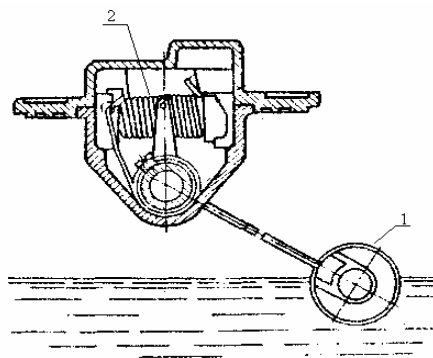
Поплавковый измерительный преобразователь: 1 – поплавок; 2 – проволочный реостат
